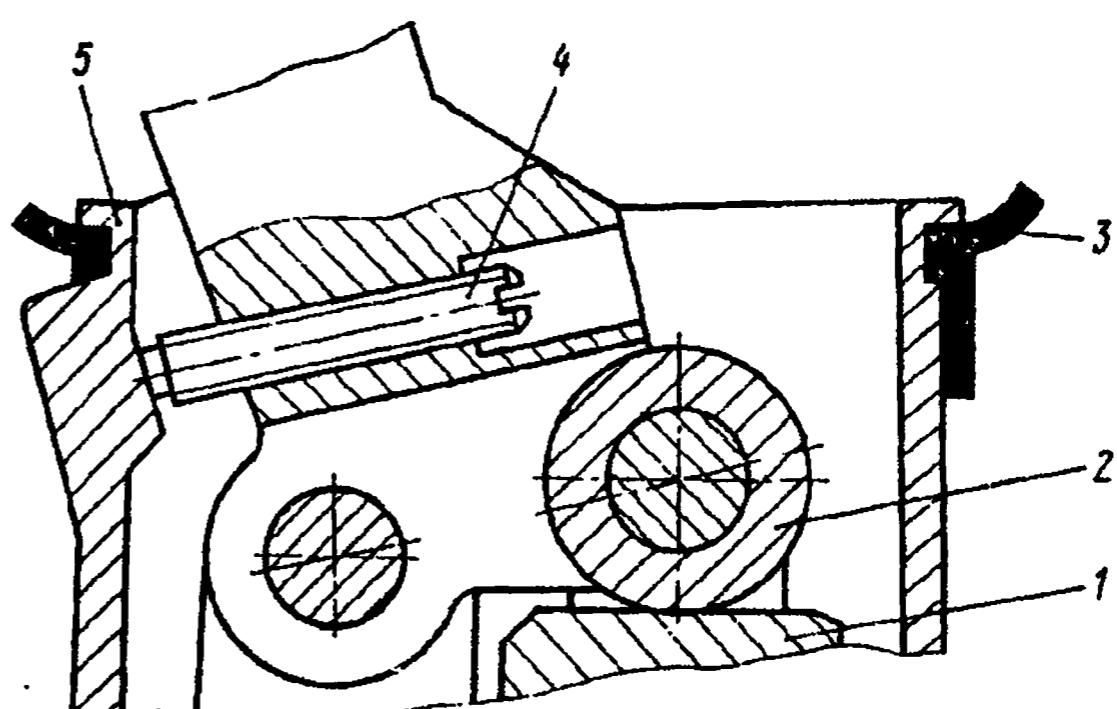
Установка регулировочного винта тормозного двухсекционного крана.
